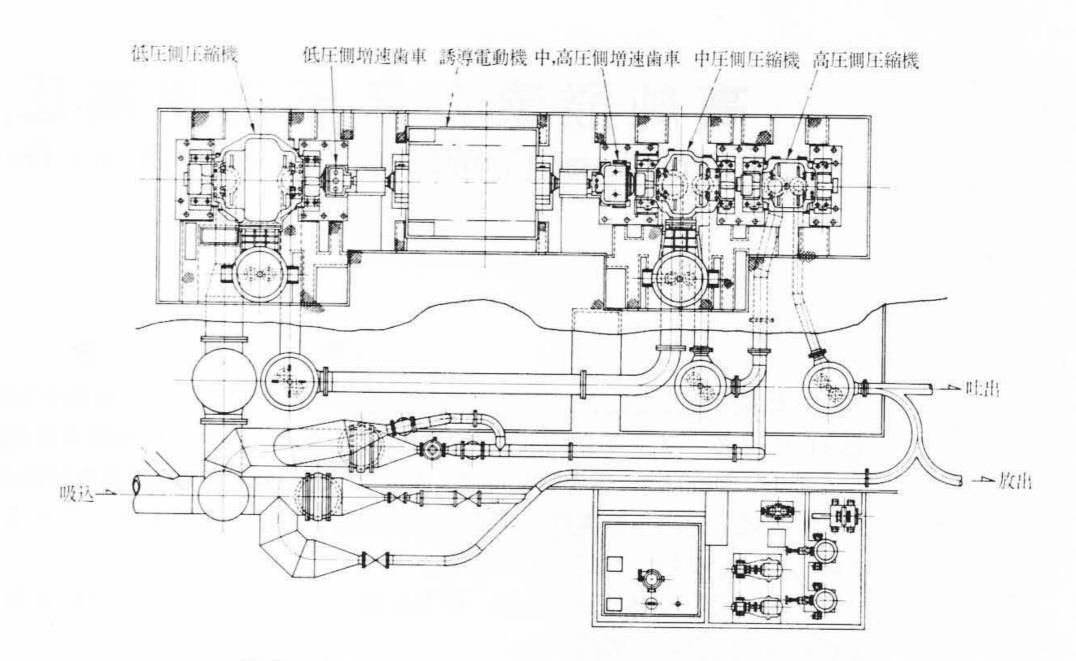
2,900 kW 遠心圧縮機,機器配置図 (平面図)
